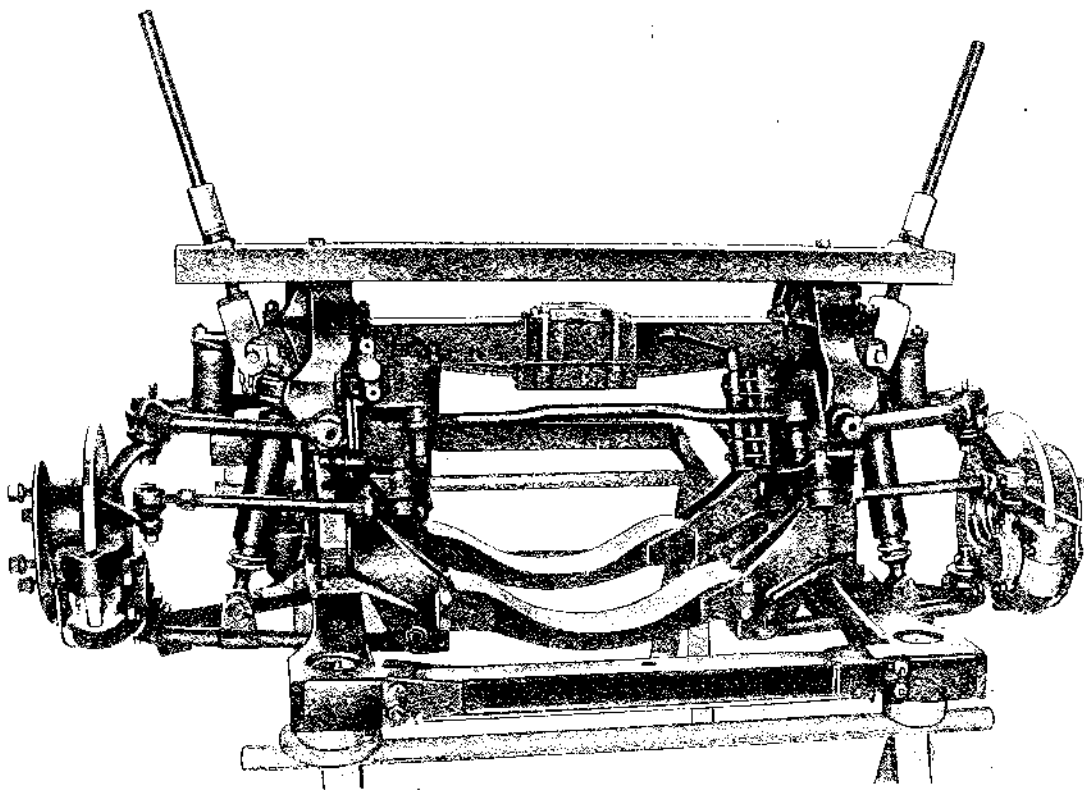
/9 - Châssis auxiliaire sur chevalets.
